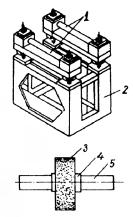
Схема балансировочного станка с параллельными валиками:
